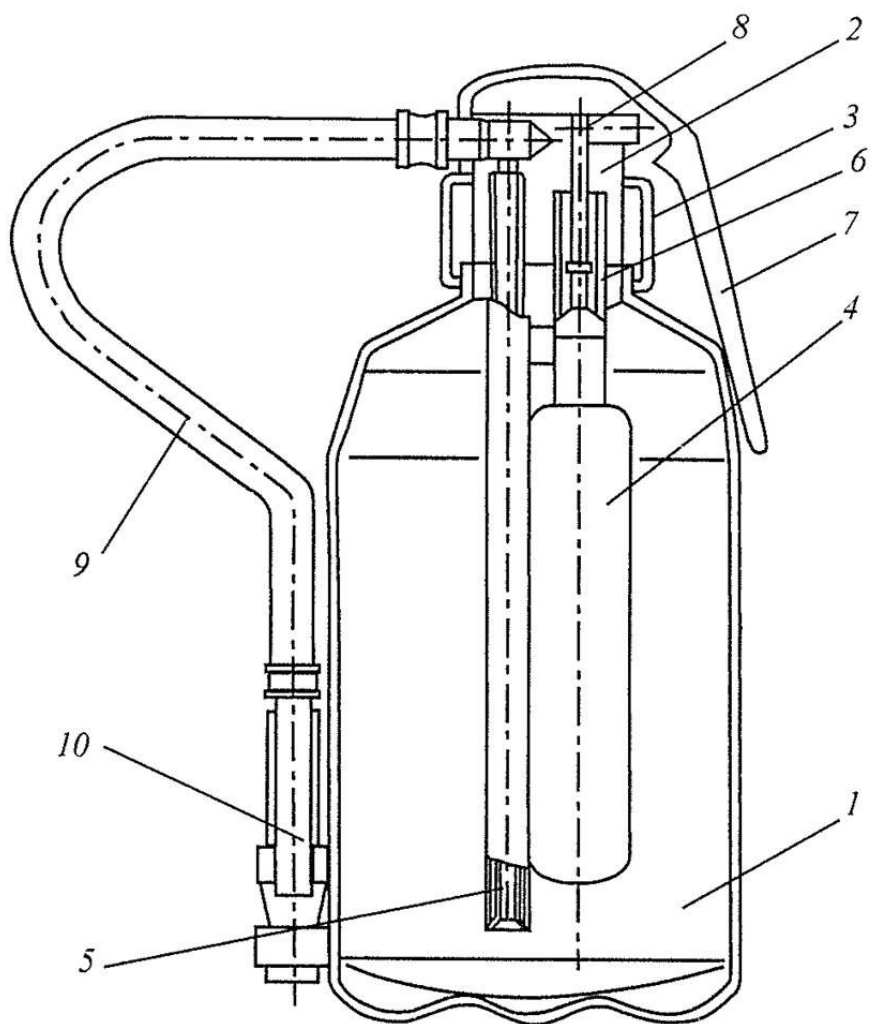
Огнетушители ОПУ-5 и ОПУ-10: 1 — корпус; 2 — гайка накидная; 3 — головка; 4 — баллон; 5 — трубка сифонная; 6 — трубка газоотводящая; 7 — рукоятка запуска; 8 — игла; 9 — рукав гибкий; 10 — распылитель пистолетный; 11 — аэроднище
